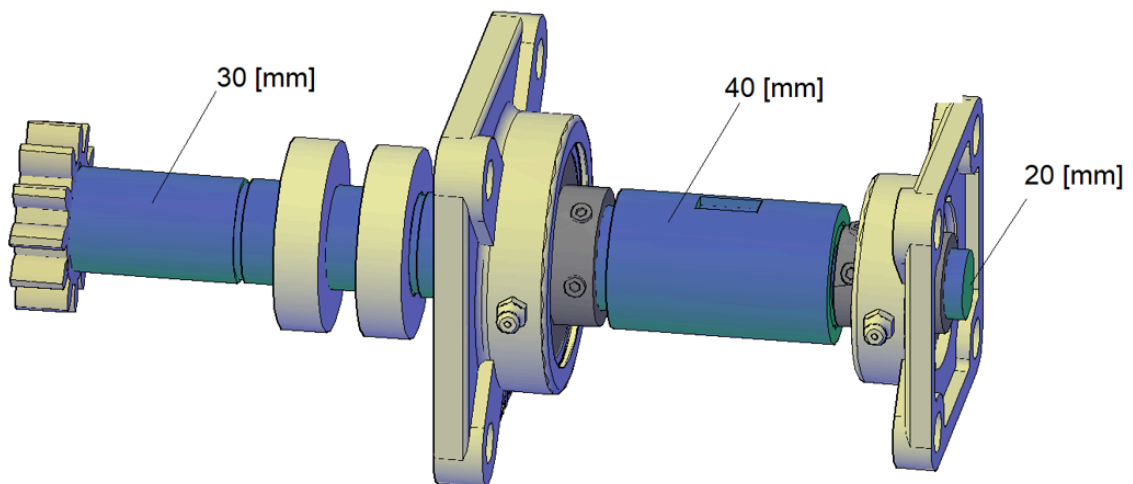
Dimensiones finales, árbol de transmisión y UCF
